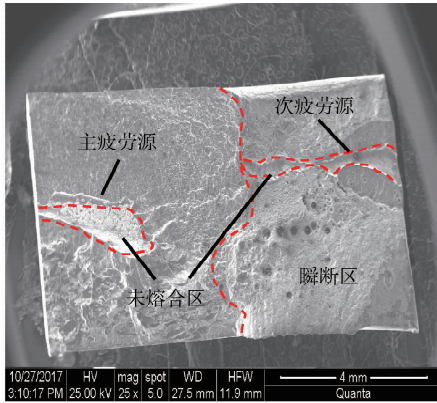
5A06-O/7A05-T6 对接接头疲劳断口(气孔缺陷)
